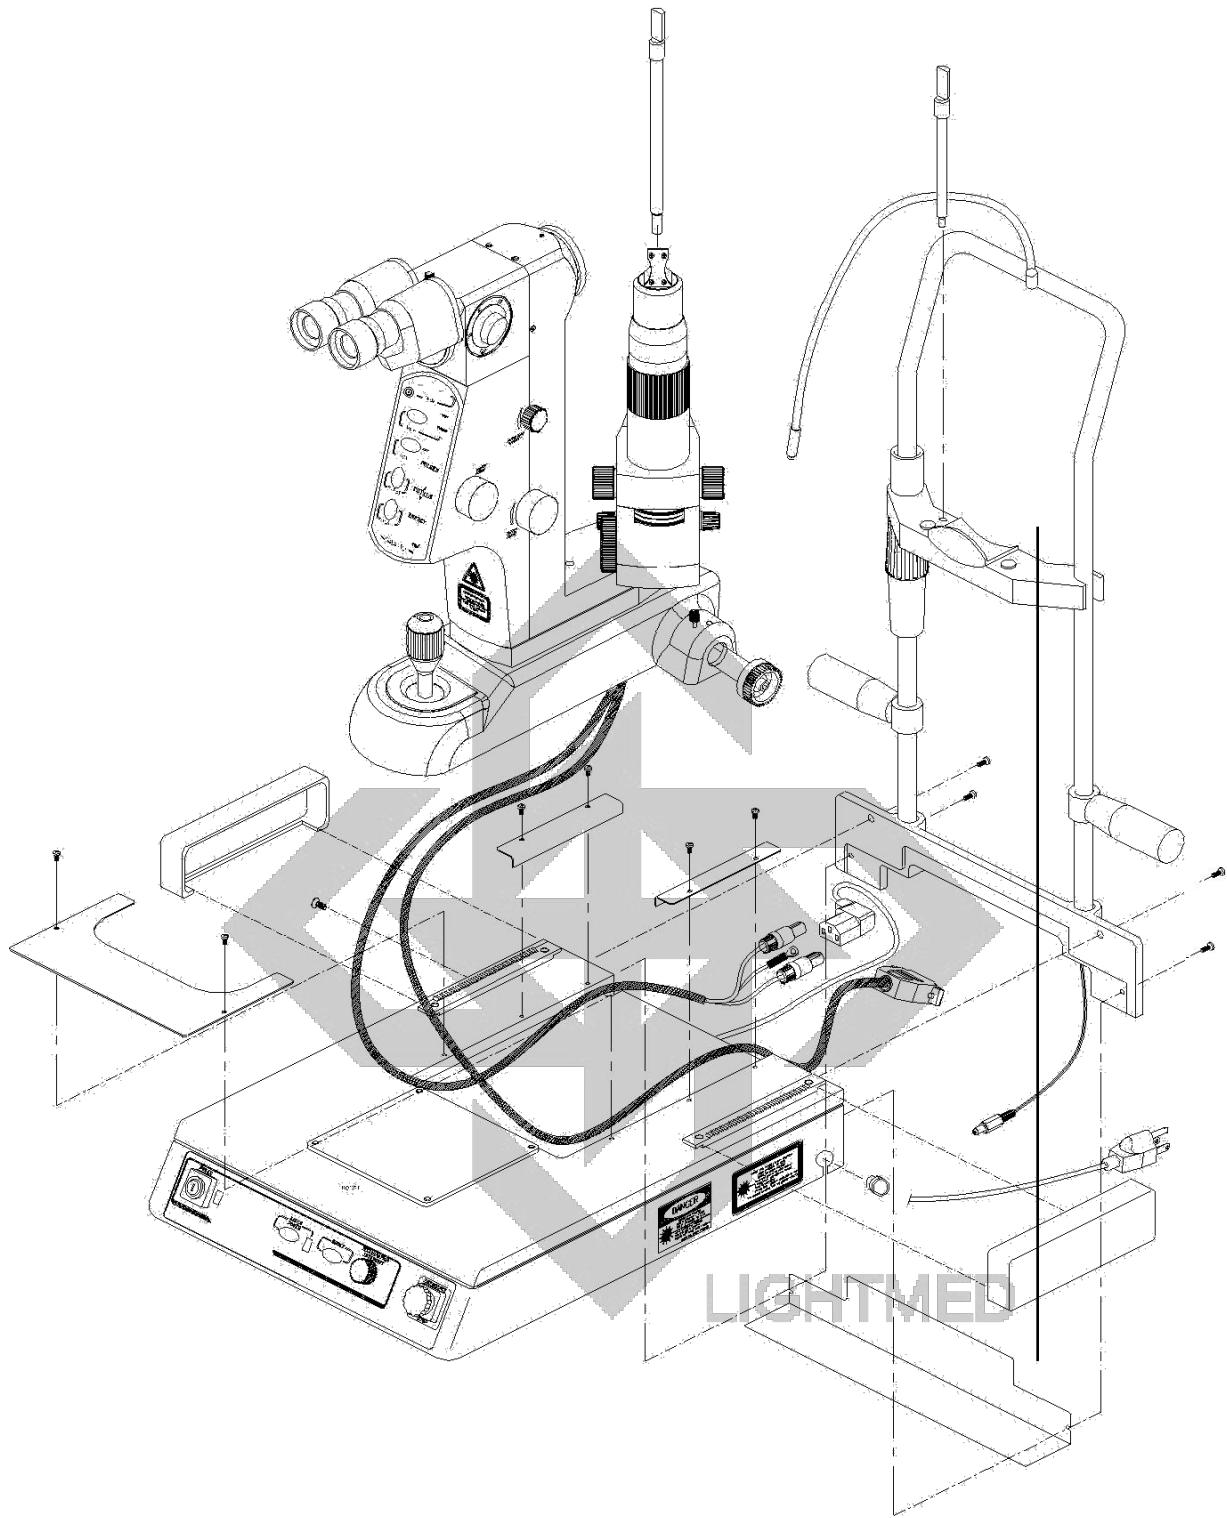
Vista Explodida das Conexões de Instalação do Sistema SELECTOR DEUX
